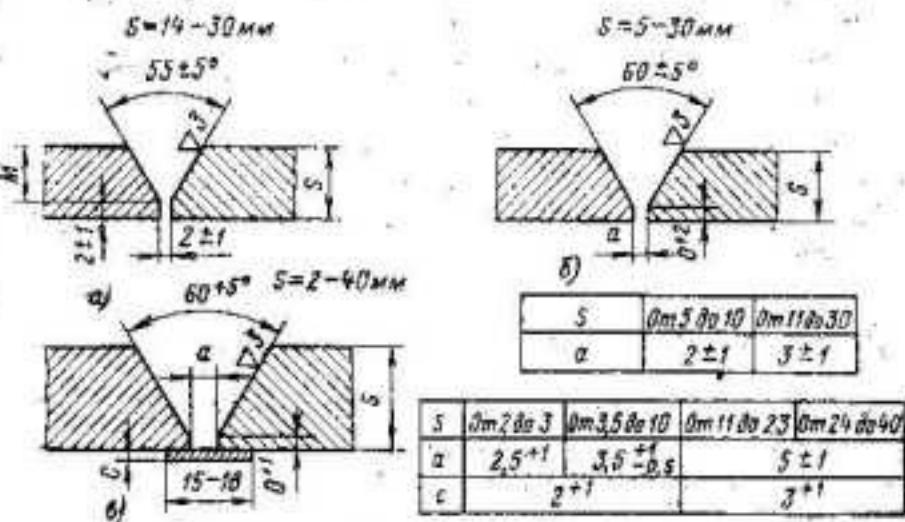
Подготовка кромок труб диаметром более 750 мм под сварку.
